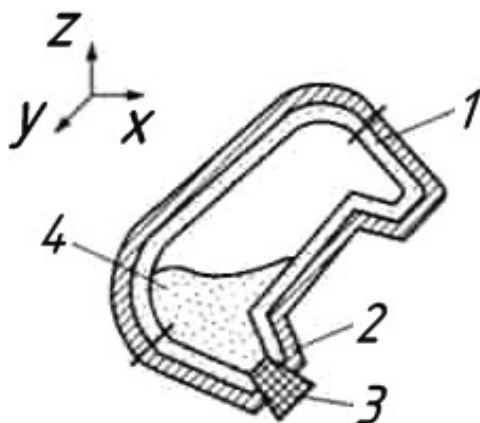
Схема изготовления оболочковых стержней Кронинг-процессом: 1 – стержень; 2 – стержневой ящик; 3 – пробка; 4 – смесь
